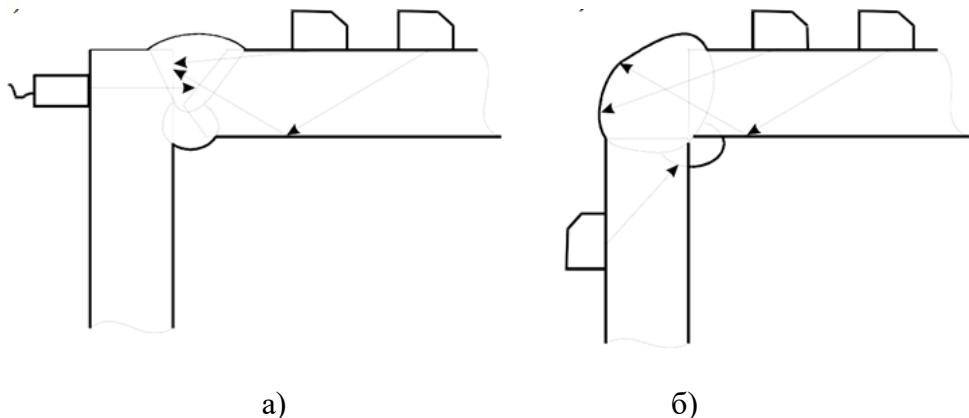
Схема контроля угловых сварных соединений
